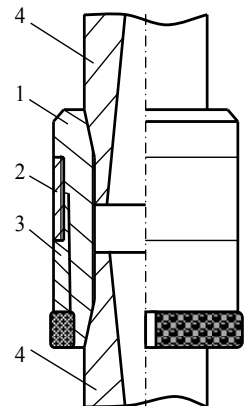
Фрезер-расширитель технологического снаряда: 1 – корпус; 2 – втулка; 3 – алмазная коронка; 4 – труба
